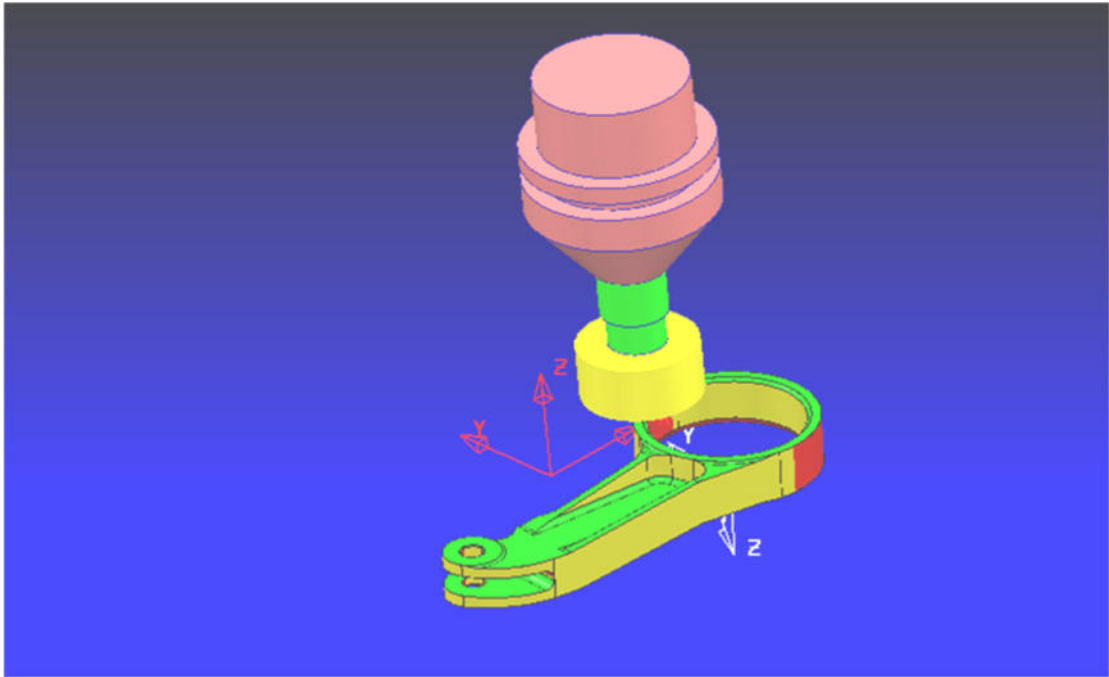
Фрезерування торцевою фрезою поверхні - 5,
